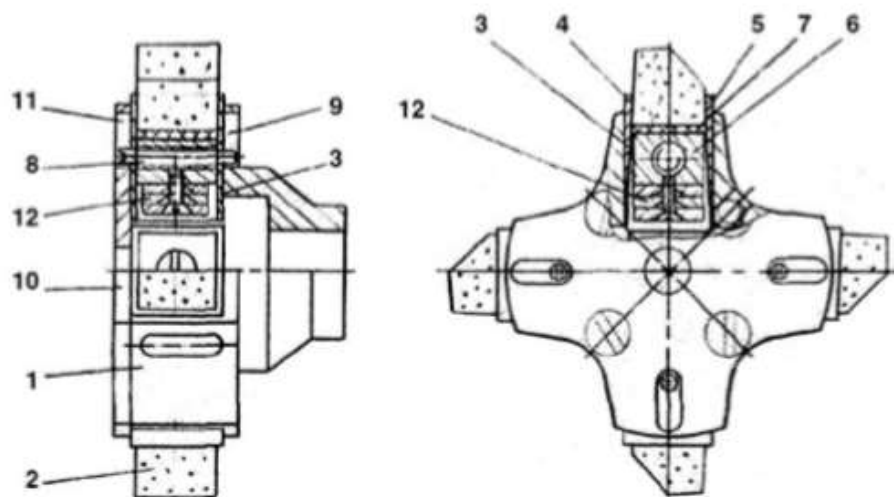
Збірний абразивний інструмент з радіально-рухливими сегментами для внутрішнього шліфування: 1 - корпус; 2 - абразивний сегмент; 3 - обойма; 4, 5 - похилі бічні ділянки абразивних сегментів; 6 - фіксатор; 7 - прокладка; 8 - вісь фіксатора; 9 - паз корпусу; 10 - кришка; 11 - паз кришки; 12 - вантаж.
